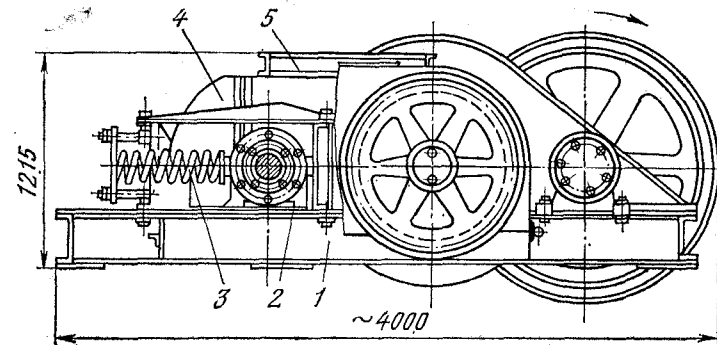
Двухвалковая дробилка зубчатая ДДЗ-4
